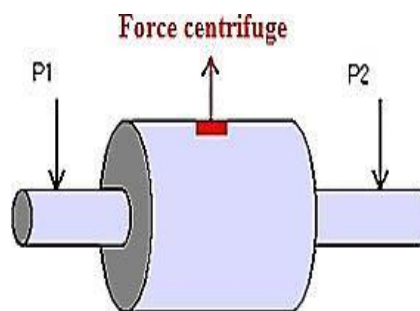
Tolérances d'usinage sur un rotor.
